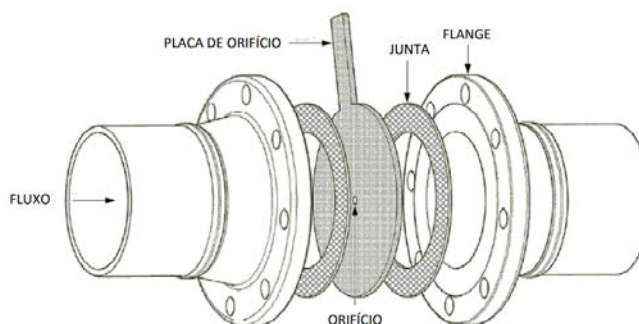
Esquema de montagem e instalação da Placa de Orifício.
